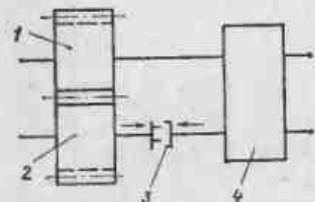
Принципиальная схема прибора для контроля кинематической погрешности зубчатых колес
